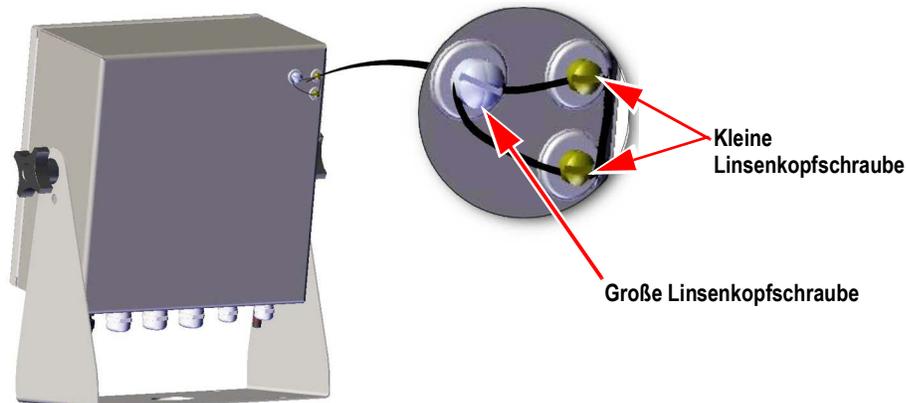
Versiegeln des Setup-Schalters (Universalgehäuse)
